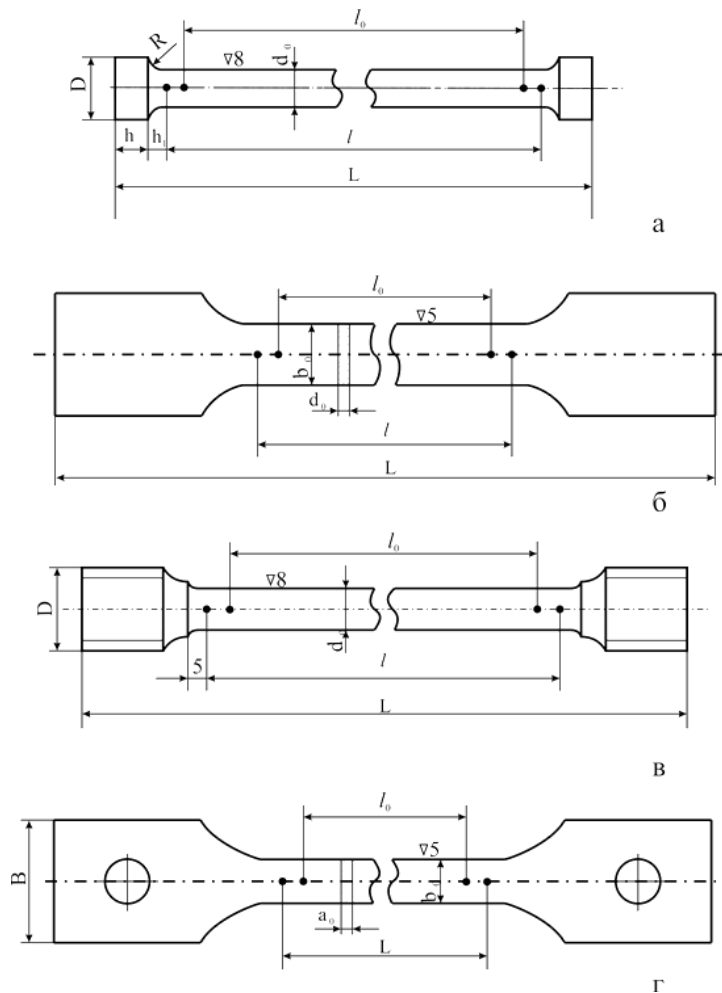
Стандартные образцы для испытаний на растяжение
